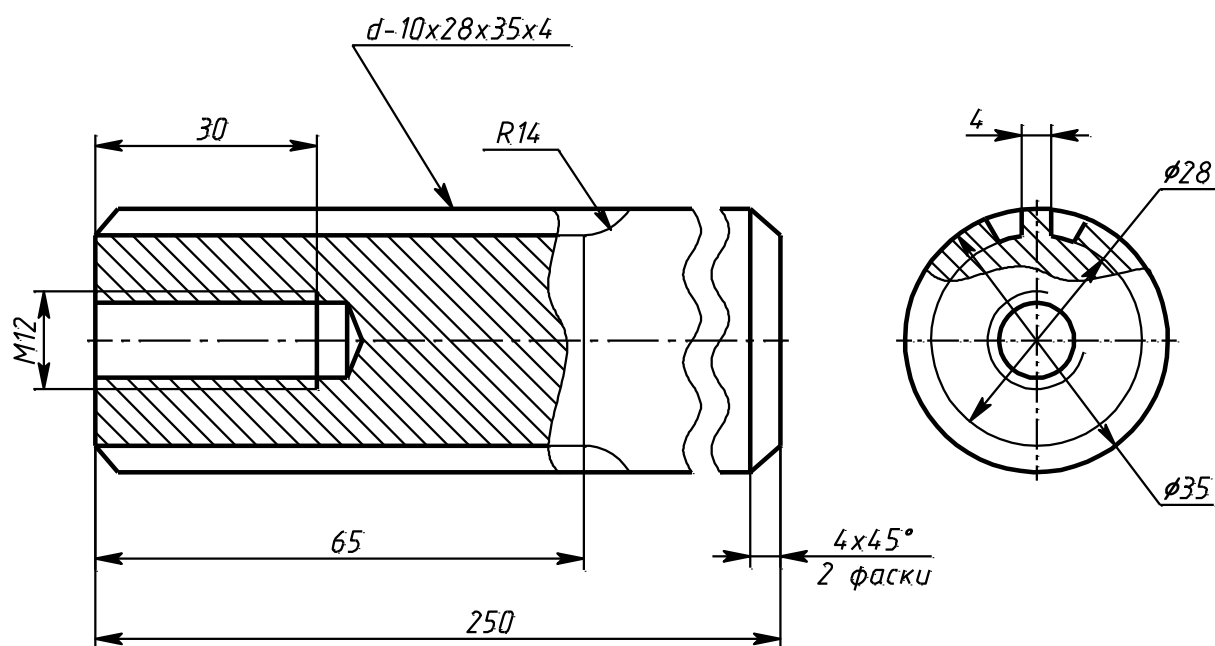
Чертеж вала для шлицевого соединения на рис 4.1
